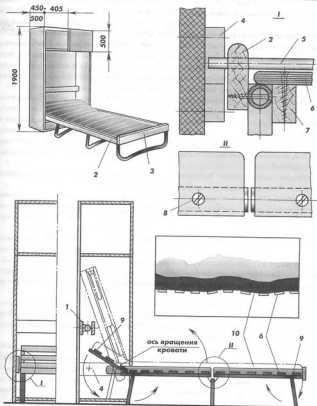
Оборудование стационарного спального места с использованием раскладной кровати
